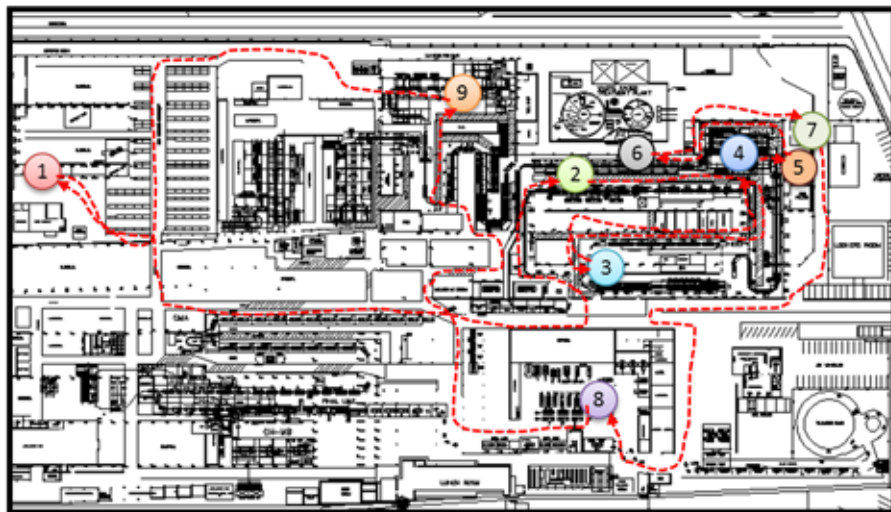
Diagrama de spaghetti del recorrido en planta propuesto
